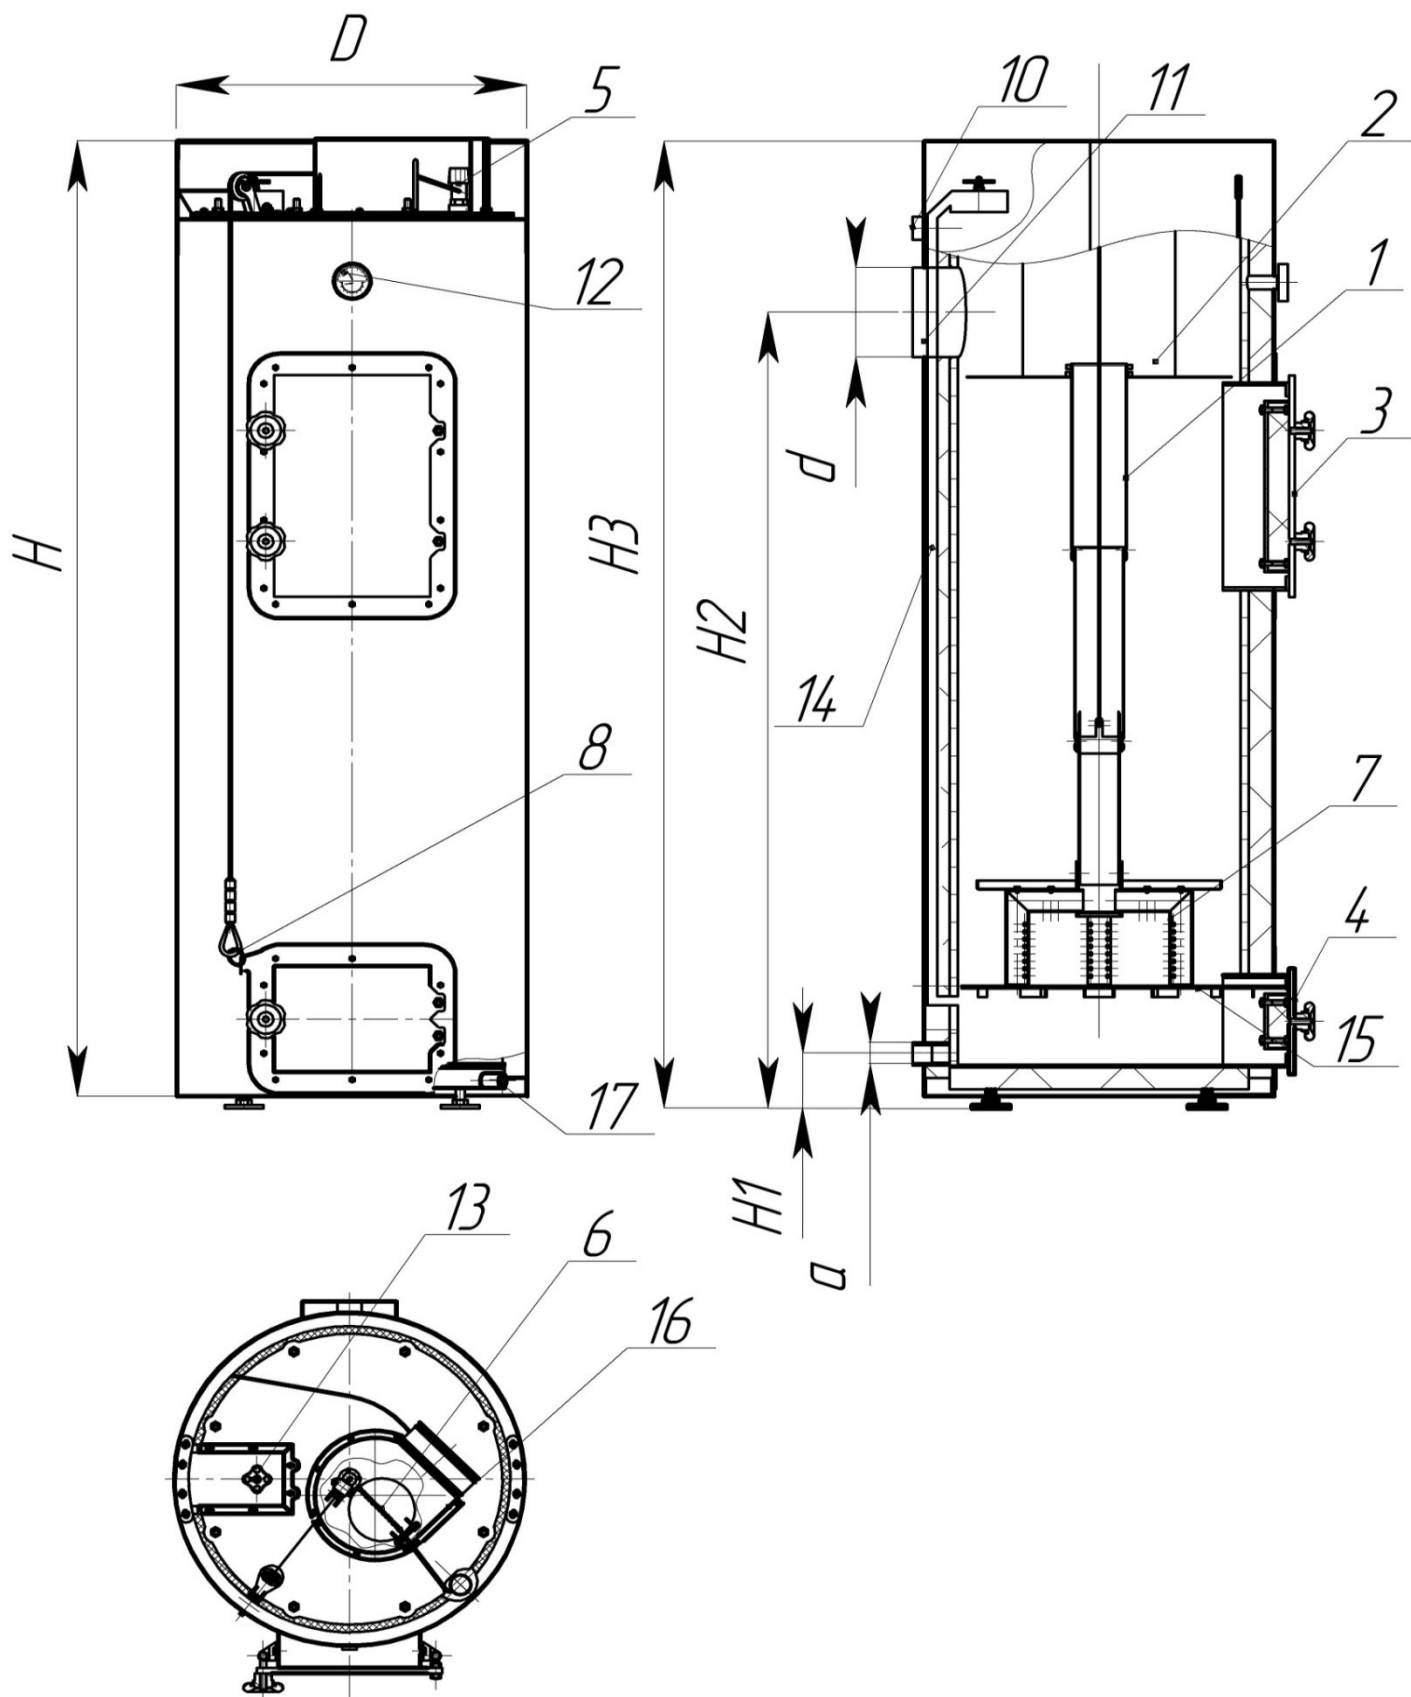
Габаритные и присоединительные размеры универсальной версии KBp-XXG/ KBp-XXGC.
